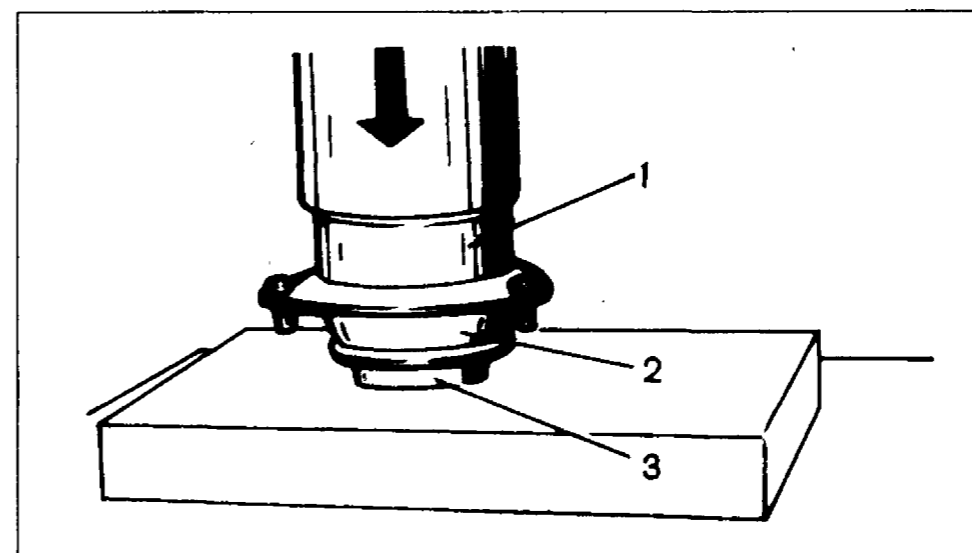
Обжим корпуса опоры: 1 — оправка; 2 — верхняя опора; 3 — упор
